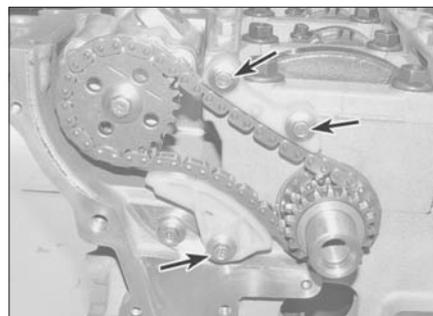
Болты (указаны стрелками) крепления направляющей и натяжителя цепи привода масляного насоса
